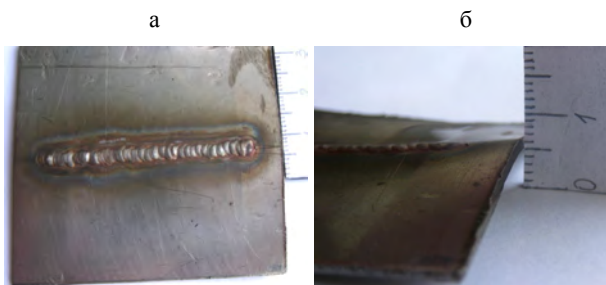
Пластина со сварным швом: а – вид сверху; б – величина деформации
